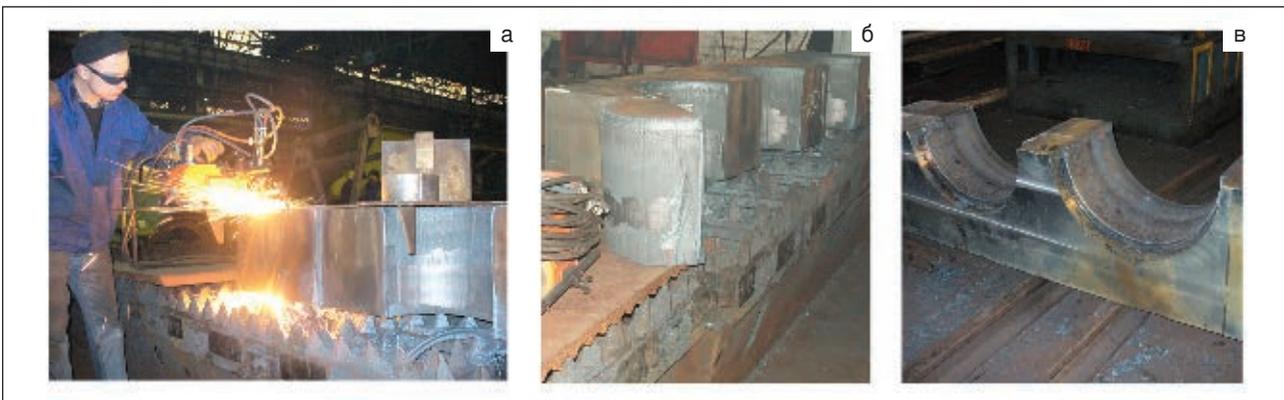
Вырезка отверстий резакон ТОРН-М (а) на заготовках корпуса подшипника из стали 40Х. Поверхность реза заготовки 320 мм, мундштук №1, диаметр режущего канала 3 мм (б). Поверхность реза заготовки 380 мм, мундштук №2, диаметр режущего канала 3,5 мм (в)
